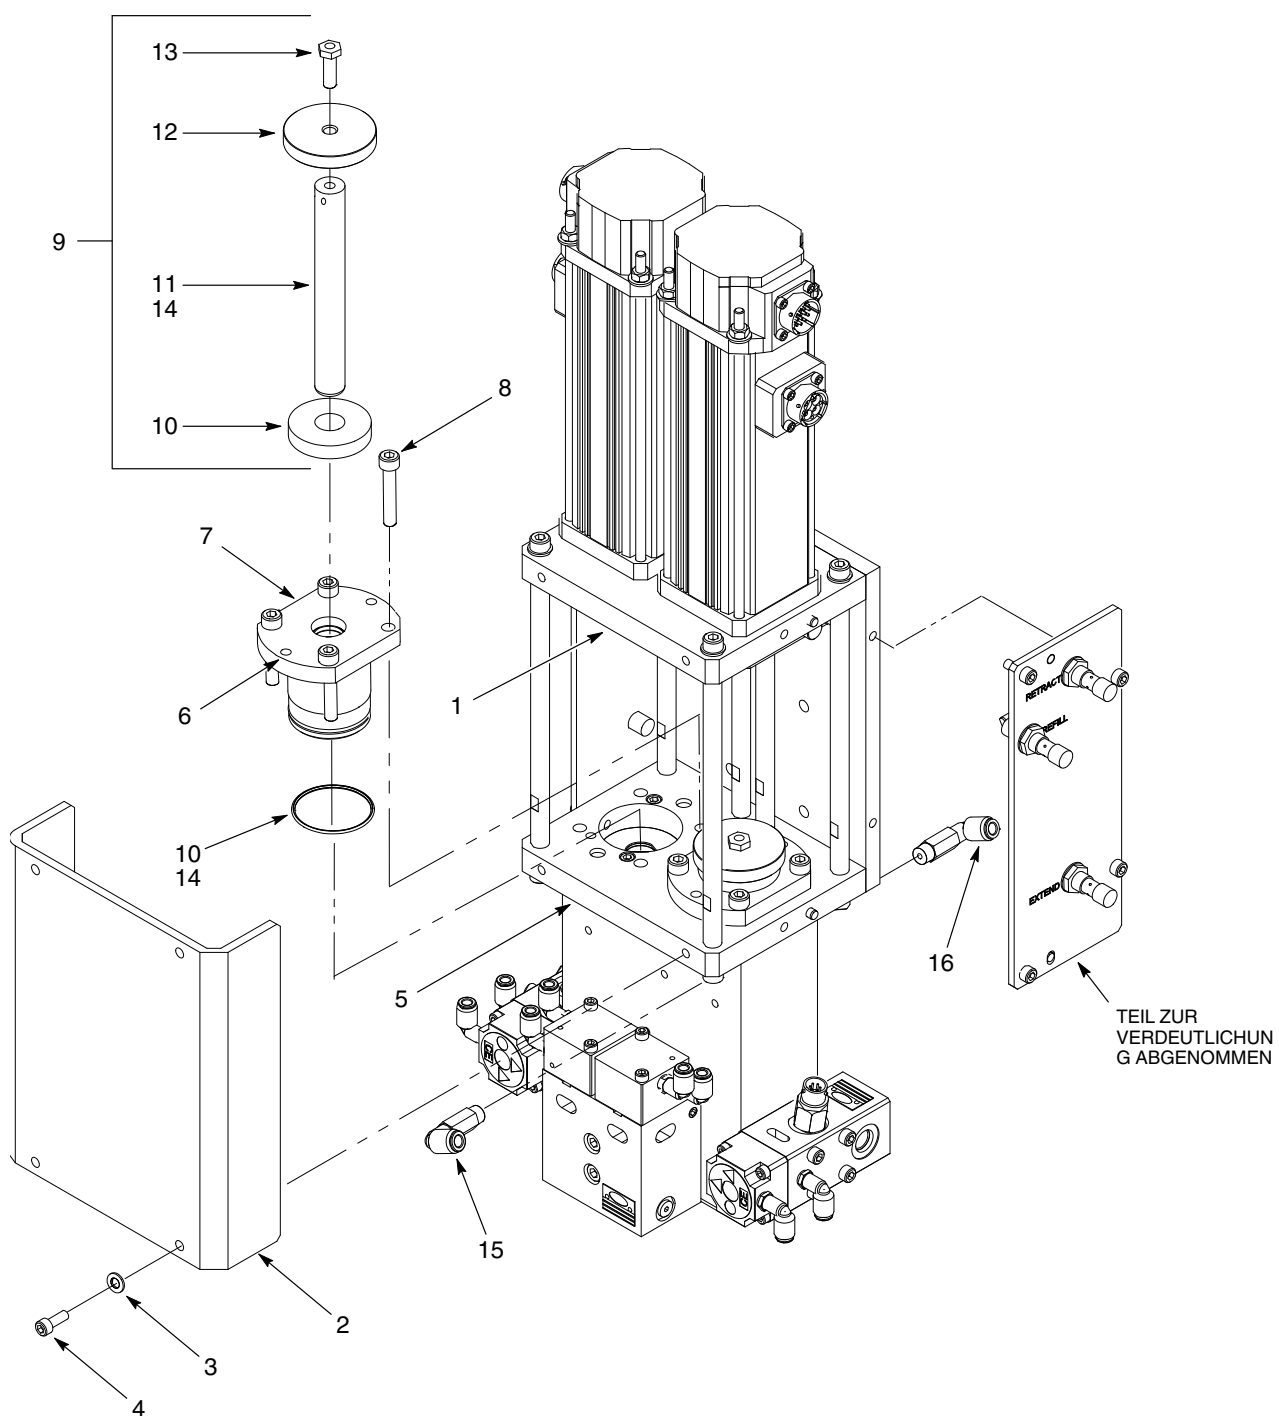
Reparaturen an Baugruppen Tauchkolben und Dichtpackung
